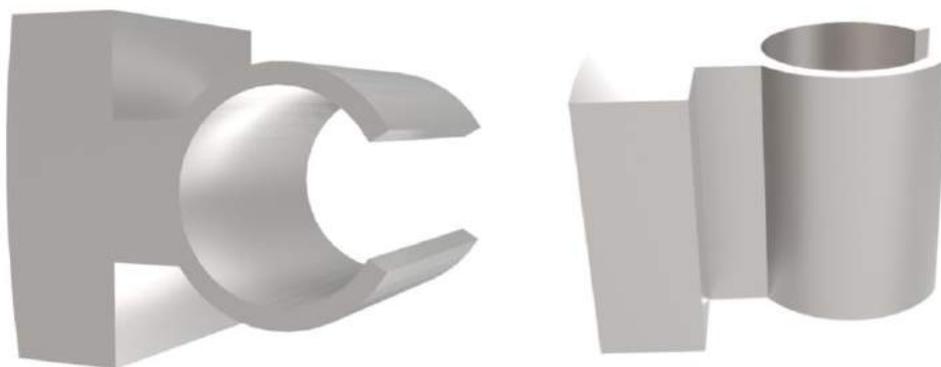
Abraçadeira em duas vistas (Fonte: elaboração própria)
